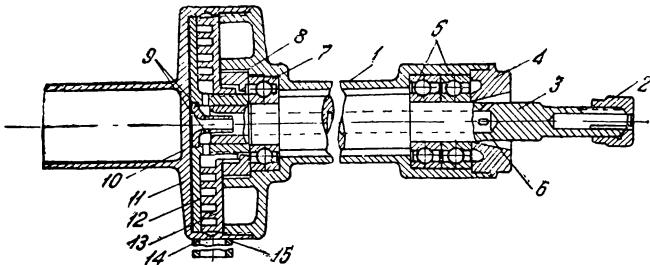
Приспособление к станку ОЗС для опиловки и шабровки (пистолет).
